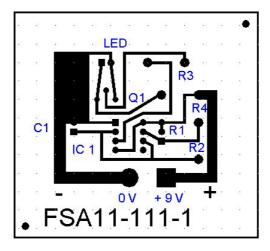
Exemple de dessin transféré à la machine-outil gravant la plaque
